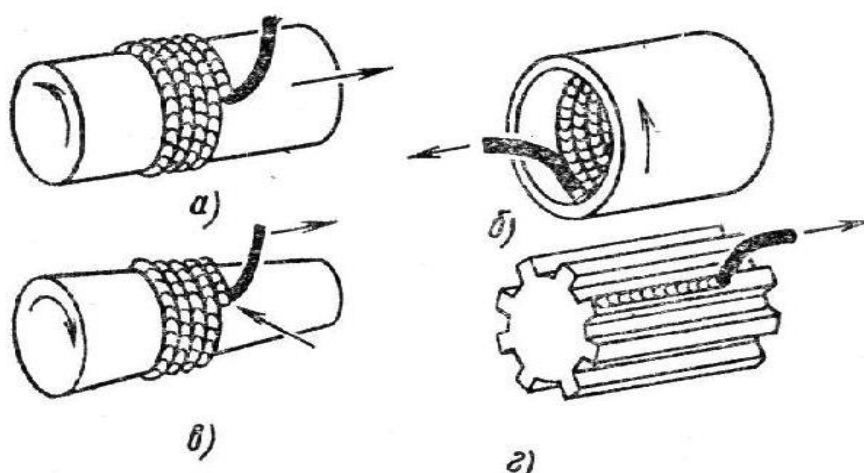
Схемы вибродуговой наплавки изделий различной формы: а – цилиндрической; б – внутренней поверхности трубы; в – конической; г – шестерни
